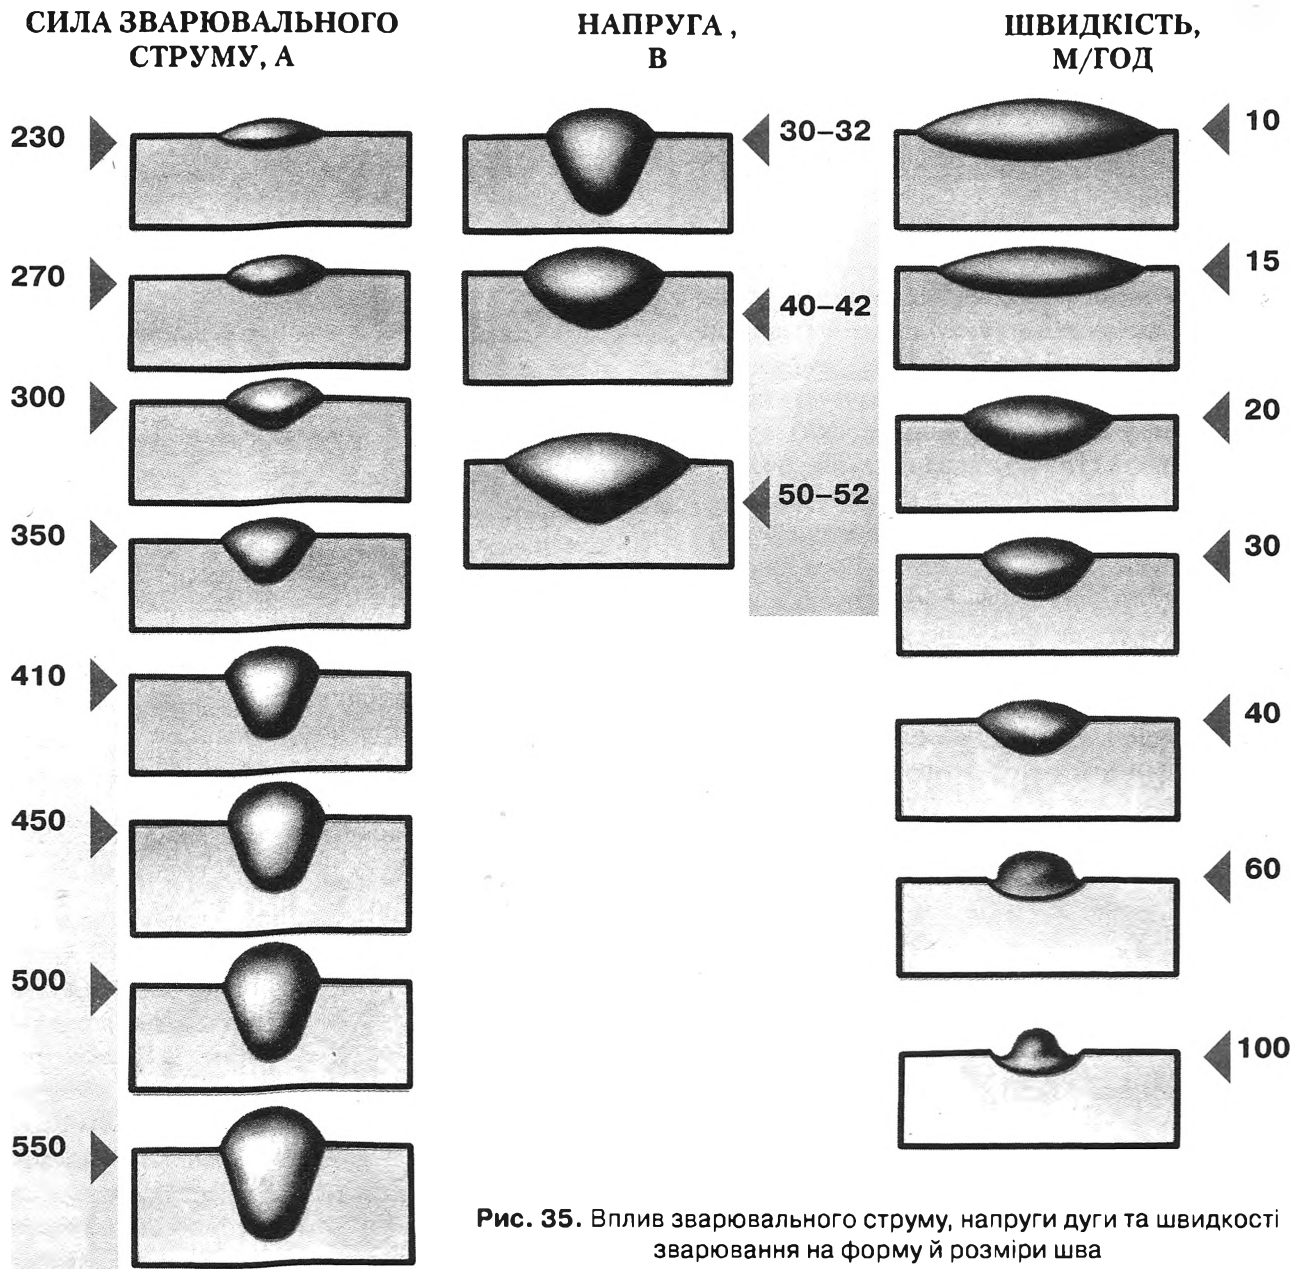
Вплив зварювального струму, напруги дуги та швидкості зварювання на форму й розміри шва
